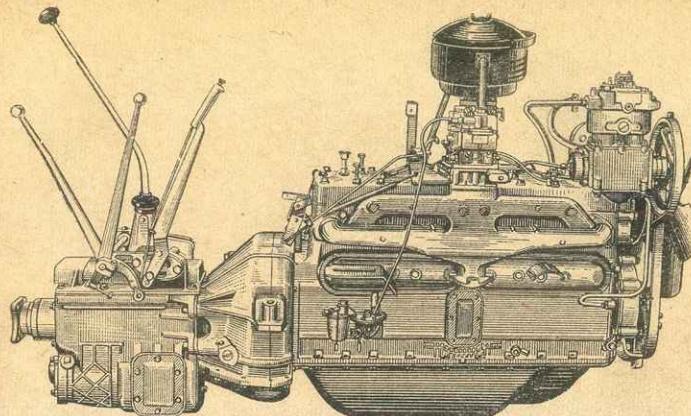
Двигатель со сцеплением и с коробкой передач (вид справа)
